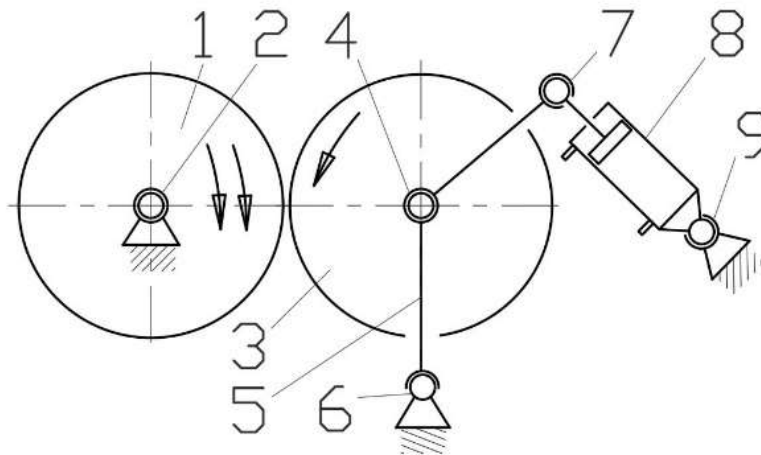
Схема двухвалкової дробарки.
